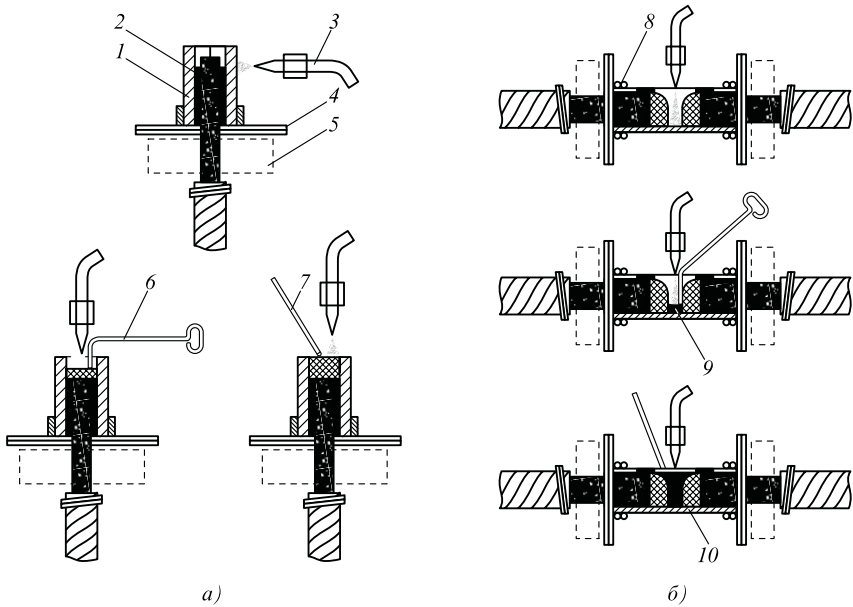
Соединение алюминиевых жил газовой сваркой:
